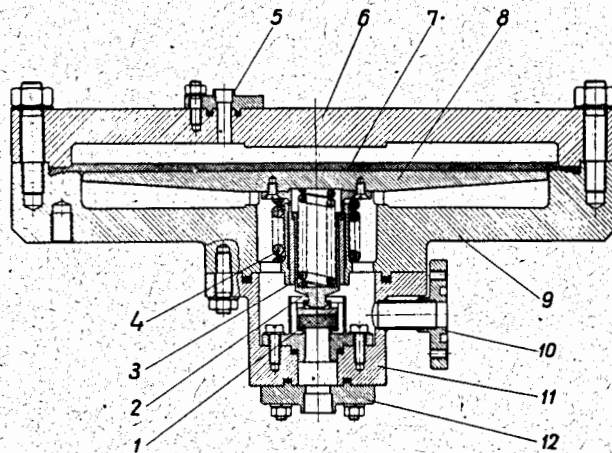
Стабилизатор давления. 1 - уплотнительный грибок; 2 - прижимная втулка; 3 - распорная пружина; 4 - возвратная пружина; 5 - выходное отверстие для газа; 6 - крышка; 7 - резиновая диафрагма; 8 - тарелка; 9 - корпус; 10 - входной патрубок; 11 - разъемная часть корпуса с седловиной; 12 - фланец выхлопной линии.
